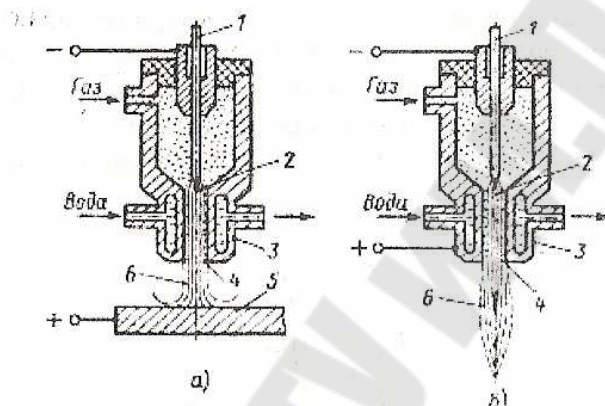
Схемы получения плазменной струи в плазмотроне прямого (а) и косвенного действия (б); 1 – вольфрамовый электрод; 2 – дуга; 3 – сопло; 4 – канал сопла; 5 – заготовка; 6 – плазменная струя
